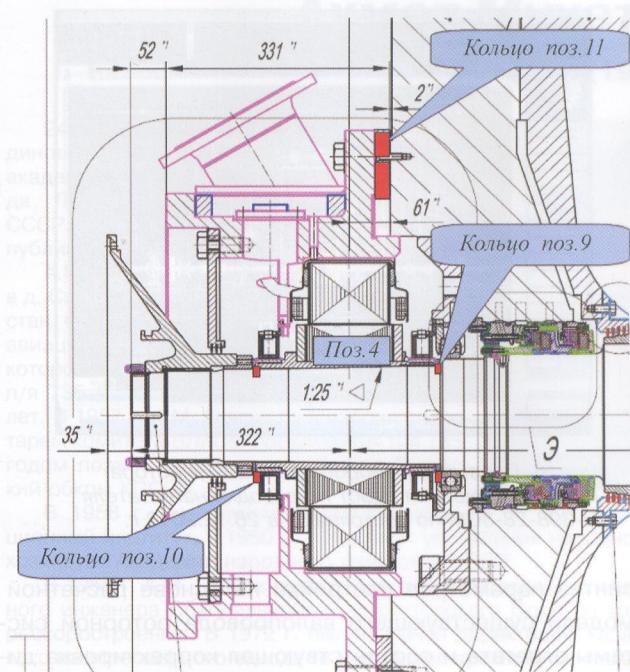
Конструкция опорного электромагнитного подшипника (сторона привода) в исполнении с винтовым зазором и дистанционными кольцами
